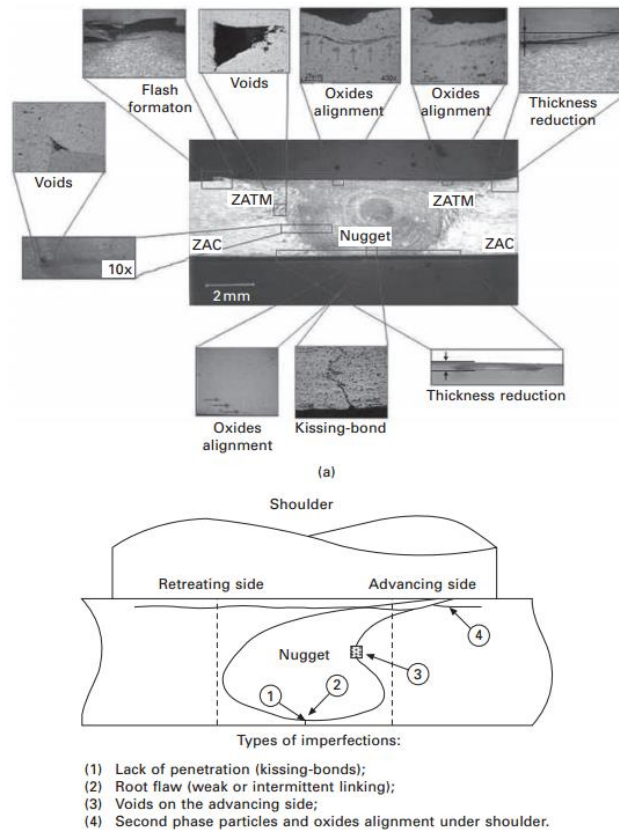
Principales defectos en soldadura FSW realizada en aluminio [92].
